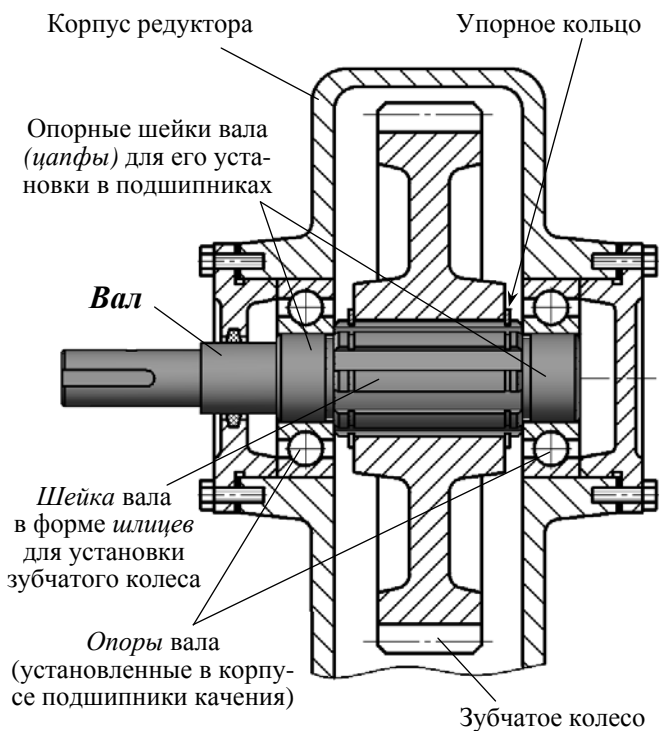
Установка зубчатого колеса в корпусе редуктора с возможностью вращения посредством вала
